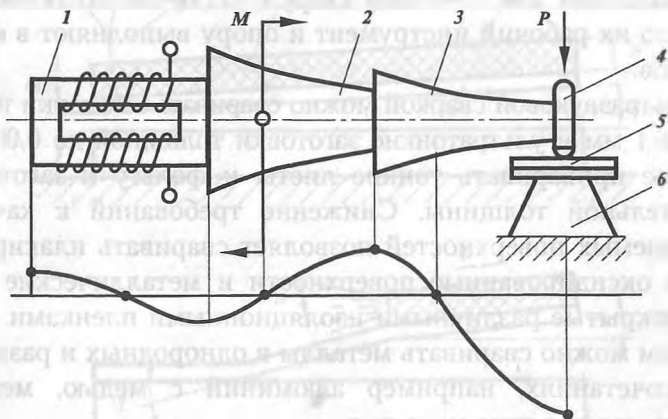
Принципиальная схема ультразвуковой сварки
